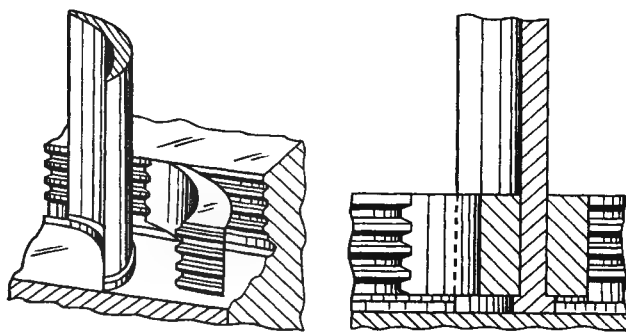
Реактивные лопатки из катаной профильной полосы
